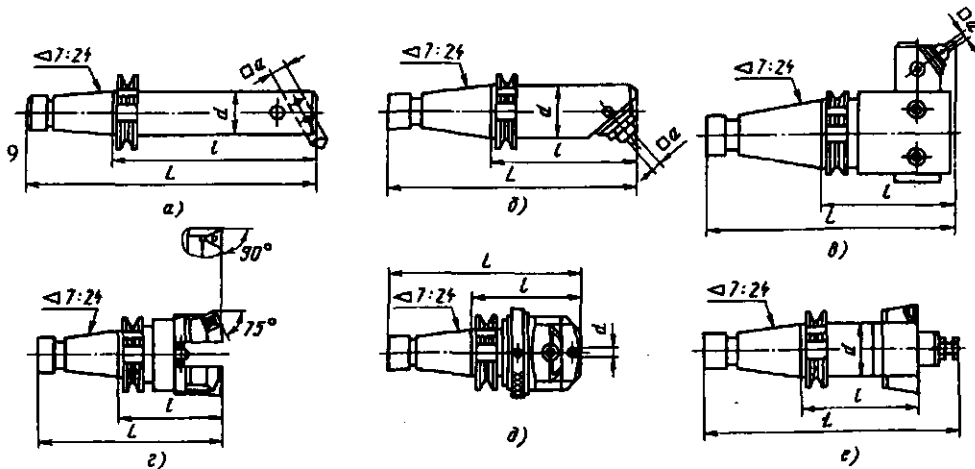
Основные типы расточных оправок для станков с ЧПУ сверлильно-фрезерно-расточной группы
